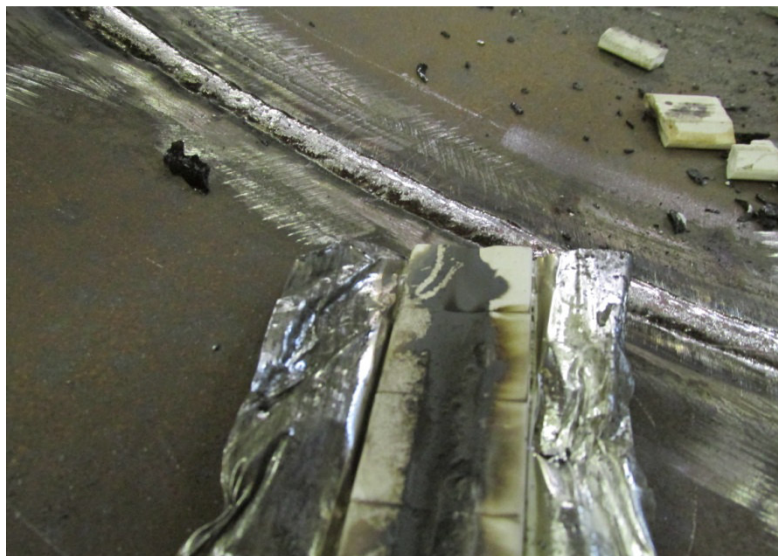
Обратный валик шва при односторонней сварке на керамической подкладке
